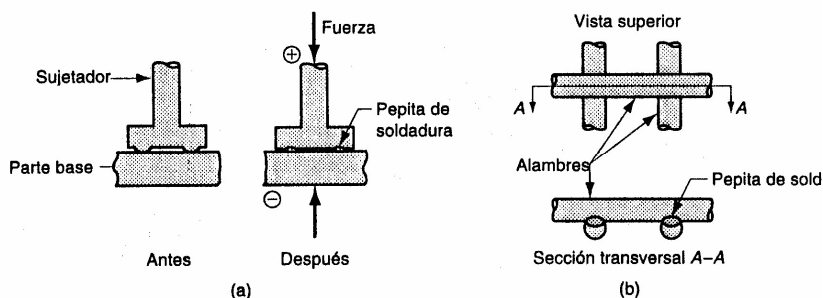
Dos variables de soldadura por proyección: (a) soldadura de un sujetador maquinado, (b) soldadura de alambre transversal.
